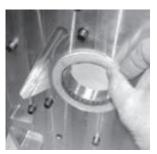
Trois pieds de centrage se trouvent à l'arrière du porte-outil à dresser pour le monter sur l'arbre principal.
